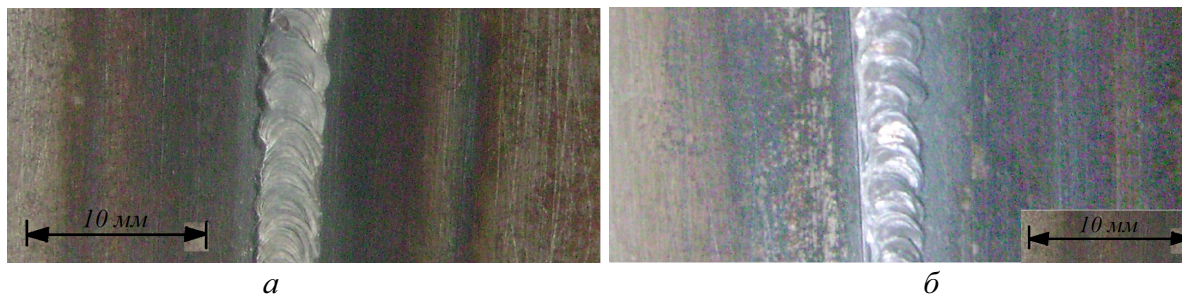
Внешний вид: а) прямой и б) обратной стороны сварного шва
